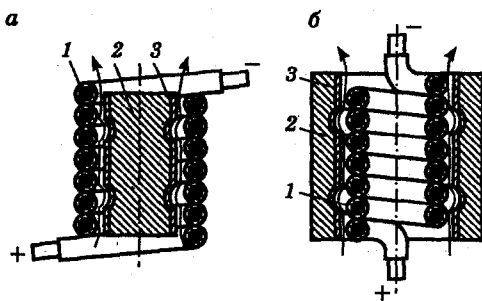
Схемы взаимного расположения обмотки индуктора, матрицы-оправки и заготовки:
